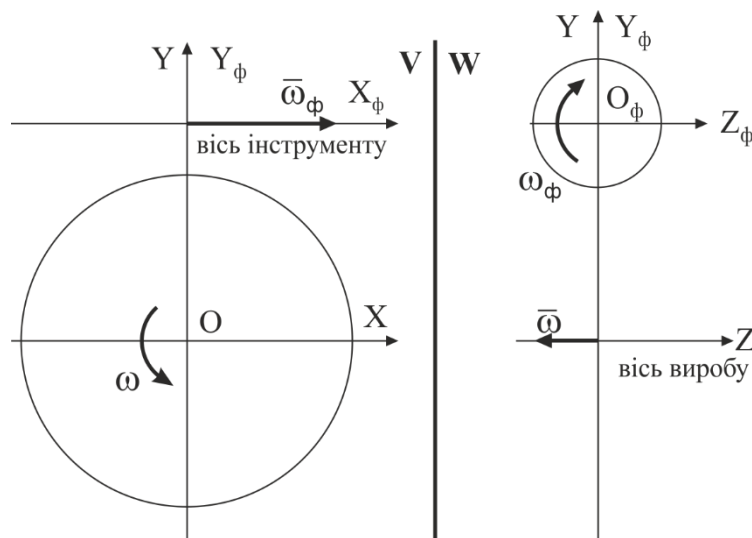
Схема обробки багатозубих виробів на зубофрезерному верстаті
